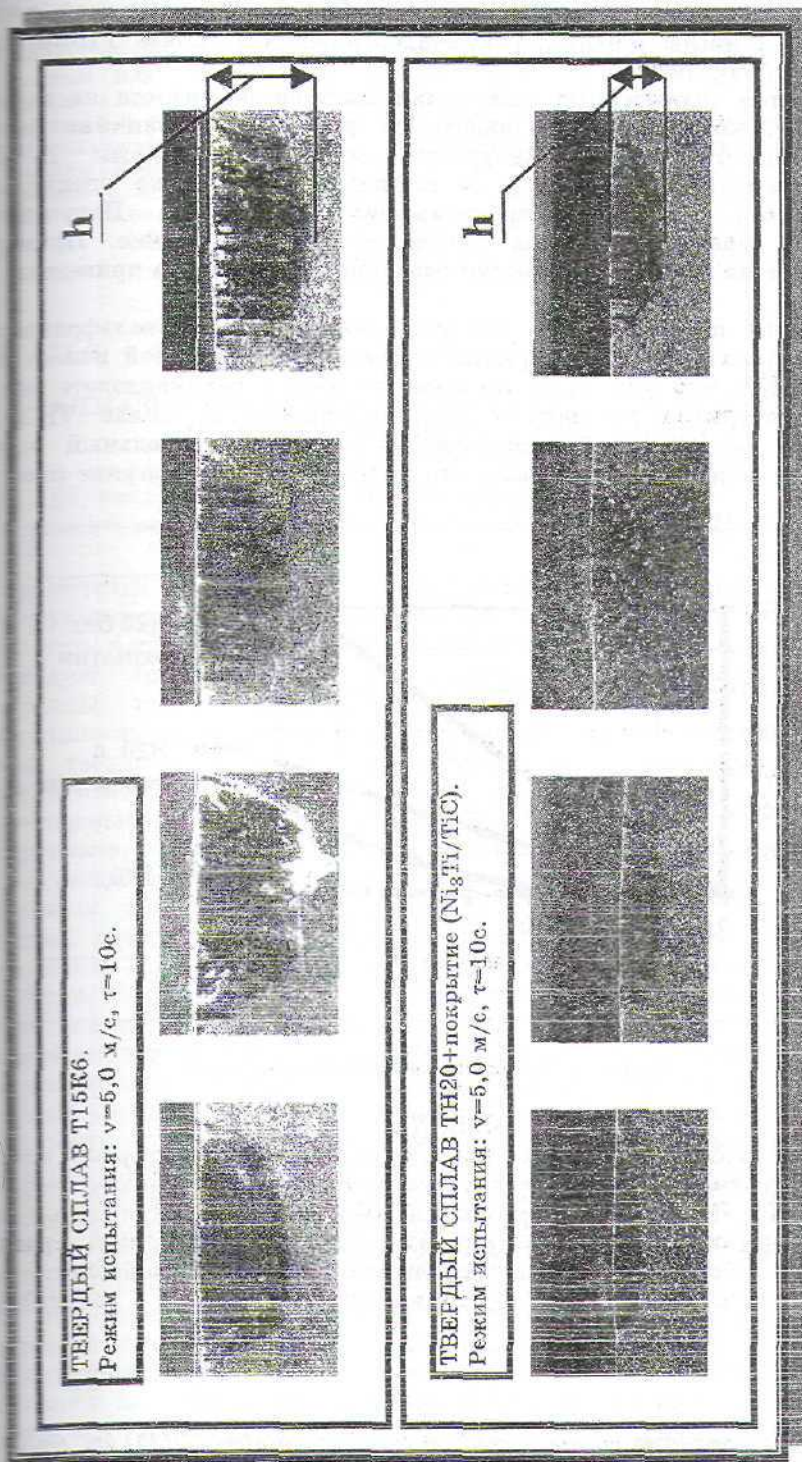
Фаски износа на задней поверхности режущего инструмента
